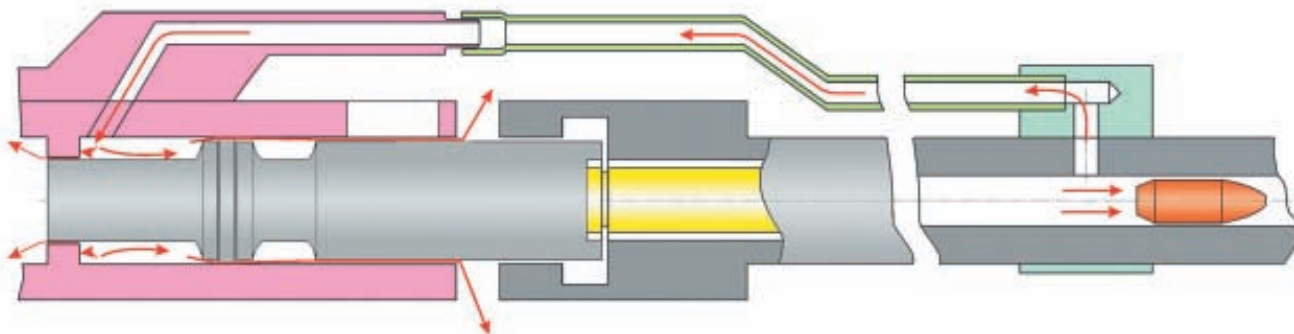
Схема БГД автоматической винтовки М16А2. Положение деталей автоматики при работе БГД. Затвор открыт. Красными стрелками показано направление истечения пороховых газов из газовой камеры.
